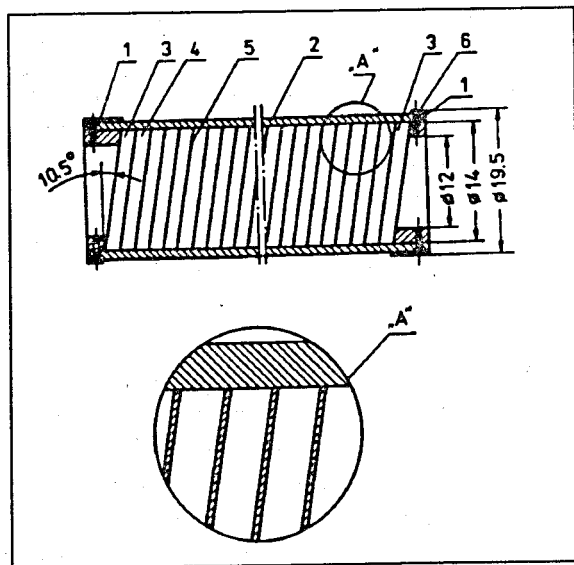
Конструкция ферромагнитного резонатора нейтронов. 1 - заслонки; 2 - корпус; 3 - пластинки из нержавеющей стали; 4 - алюминиевые прокладки; 5 - фольги пермаллоя; 6 - фиксирующие болты.
